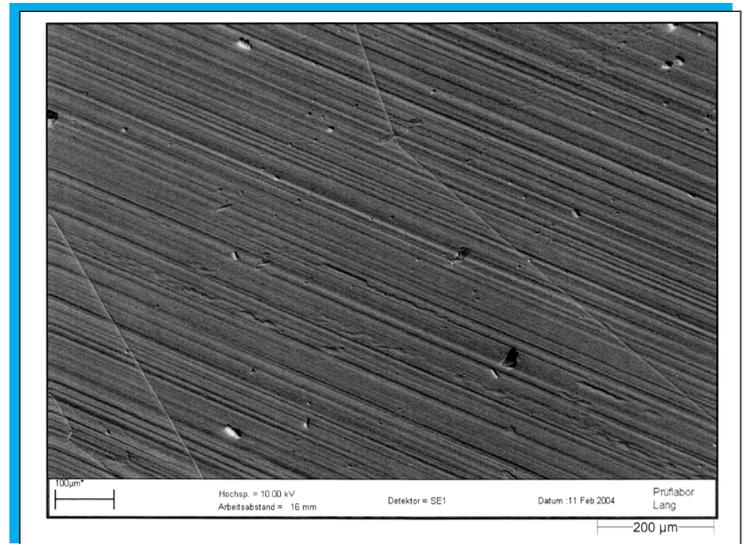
Zahnflanke; REM-Aufnahme nach ca. 1.000 h Einsatz mit herkömmlichem CLP-Öl, beginnende Mikroanrisse und Pittingbildung bereits sichtbar (Fehlstellen sind untersuchungstechnisch bedingt), kaum Glättung
